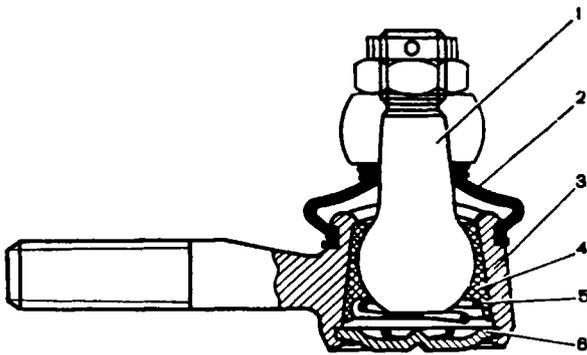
Разрез шарового шарнира тяги: 1 - шаровой палец; 2 - грязезащитный колпачок; 3 - корпус шарнира; 4 - вкладыш; 5 - пружина; 6 - заглушка
